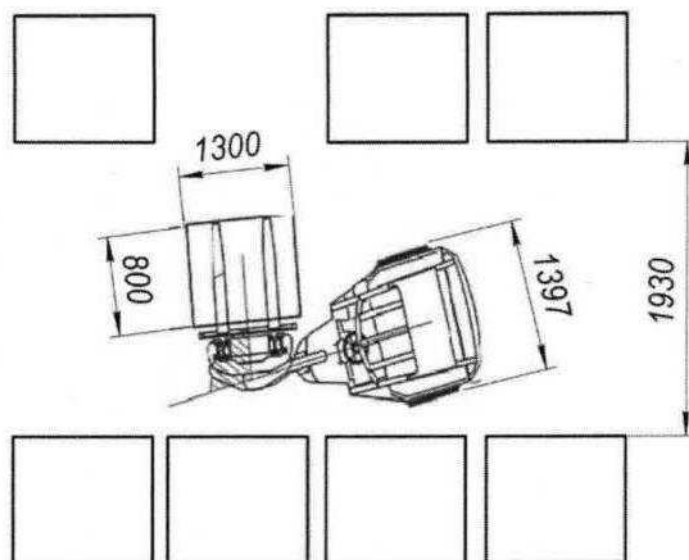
Общий вид узкопроходного погрузчика Bendi B45SE с габаритными размерами
